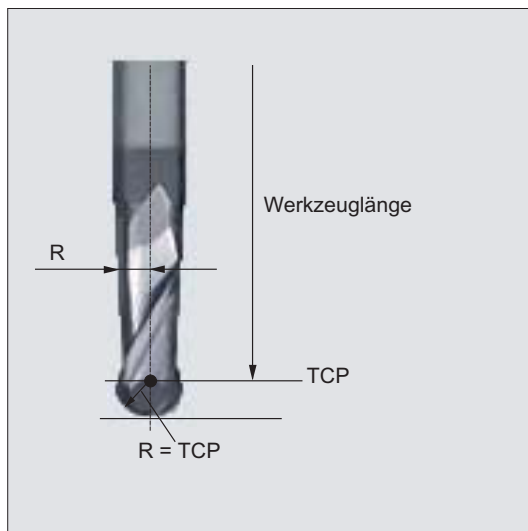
Als Werkzeuglänge des Radienfräasers muss die Länge bis zum TCP (Tool Center Point) eingegeben werden.
